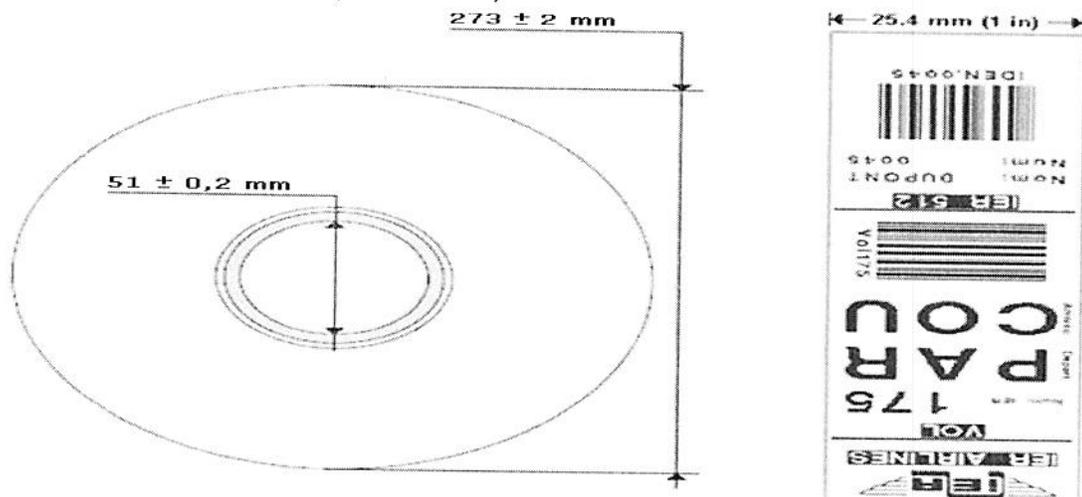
Dimensiones del rollo de papel termo sensible
